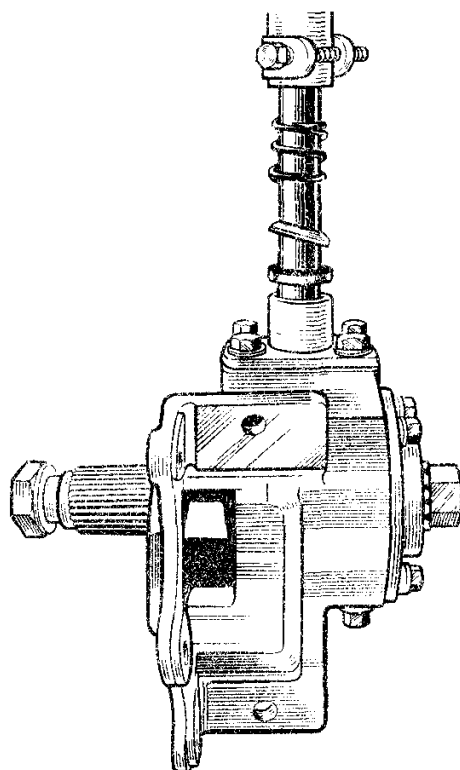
Снятие трубы колонки, пружины, опорной шайбы и уплотнительного кольца
